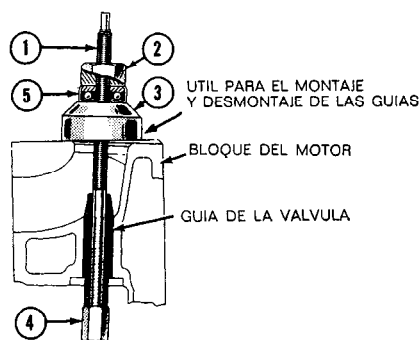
La guía de la válvula se desmonta del motor por medio de un extractor: (1) tornillo; (2) tuerca; (3) espaciador de apoyo; (4) tuerca de empuje; (5) cojinete.
